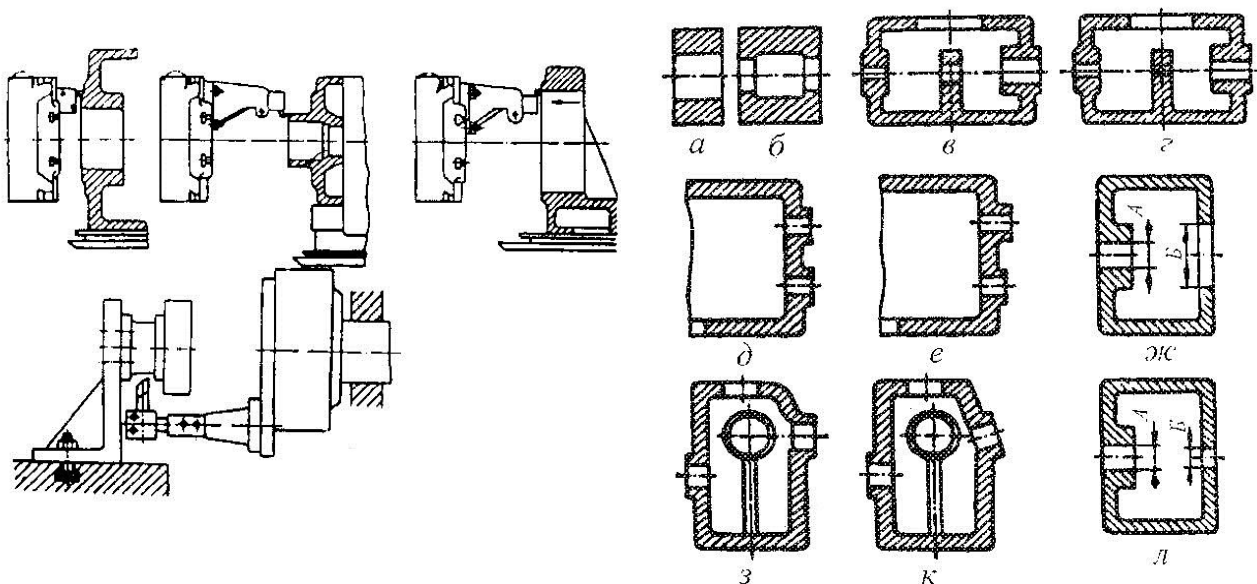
Схеми обробки різцями на розточувальних верстатах
